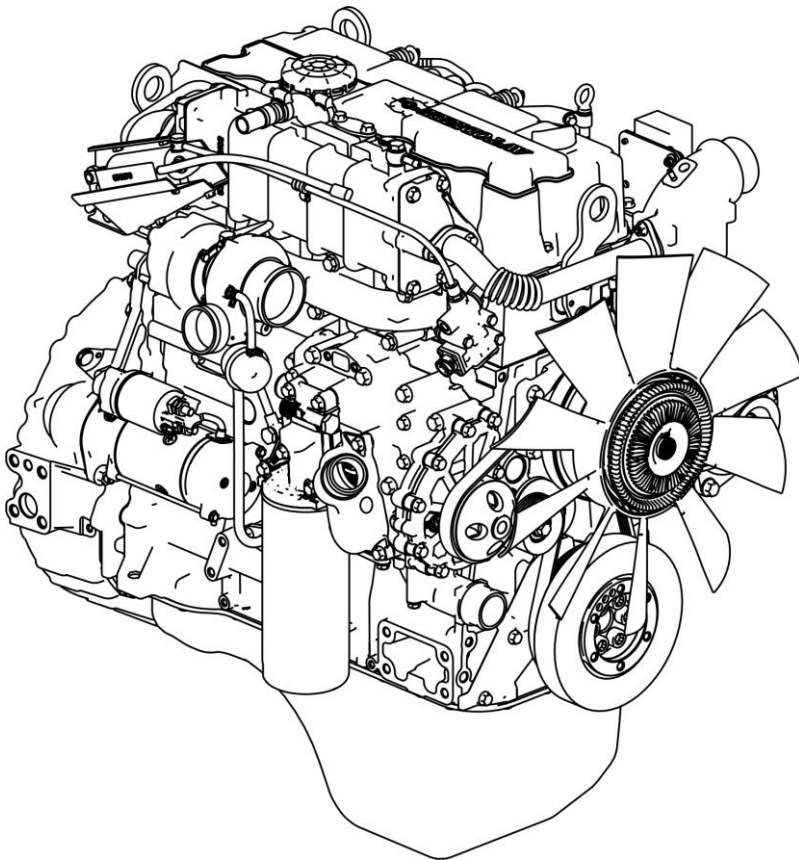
Двигатель ЯМЗ-53443-21 (общий вид справа)
